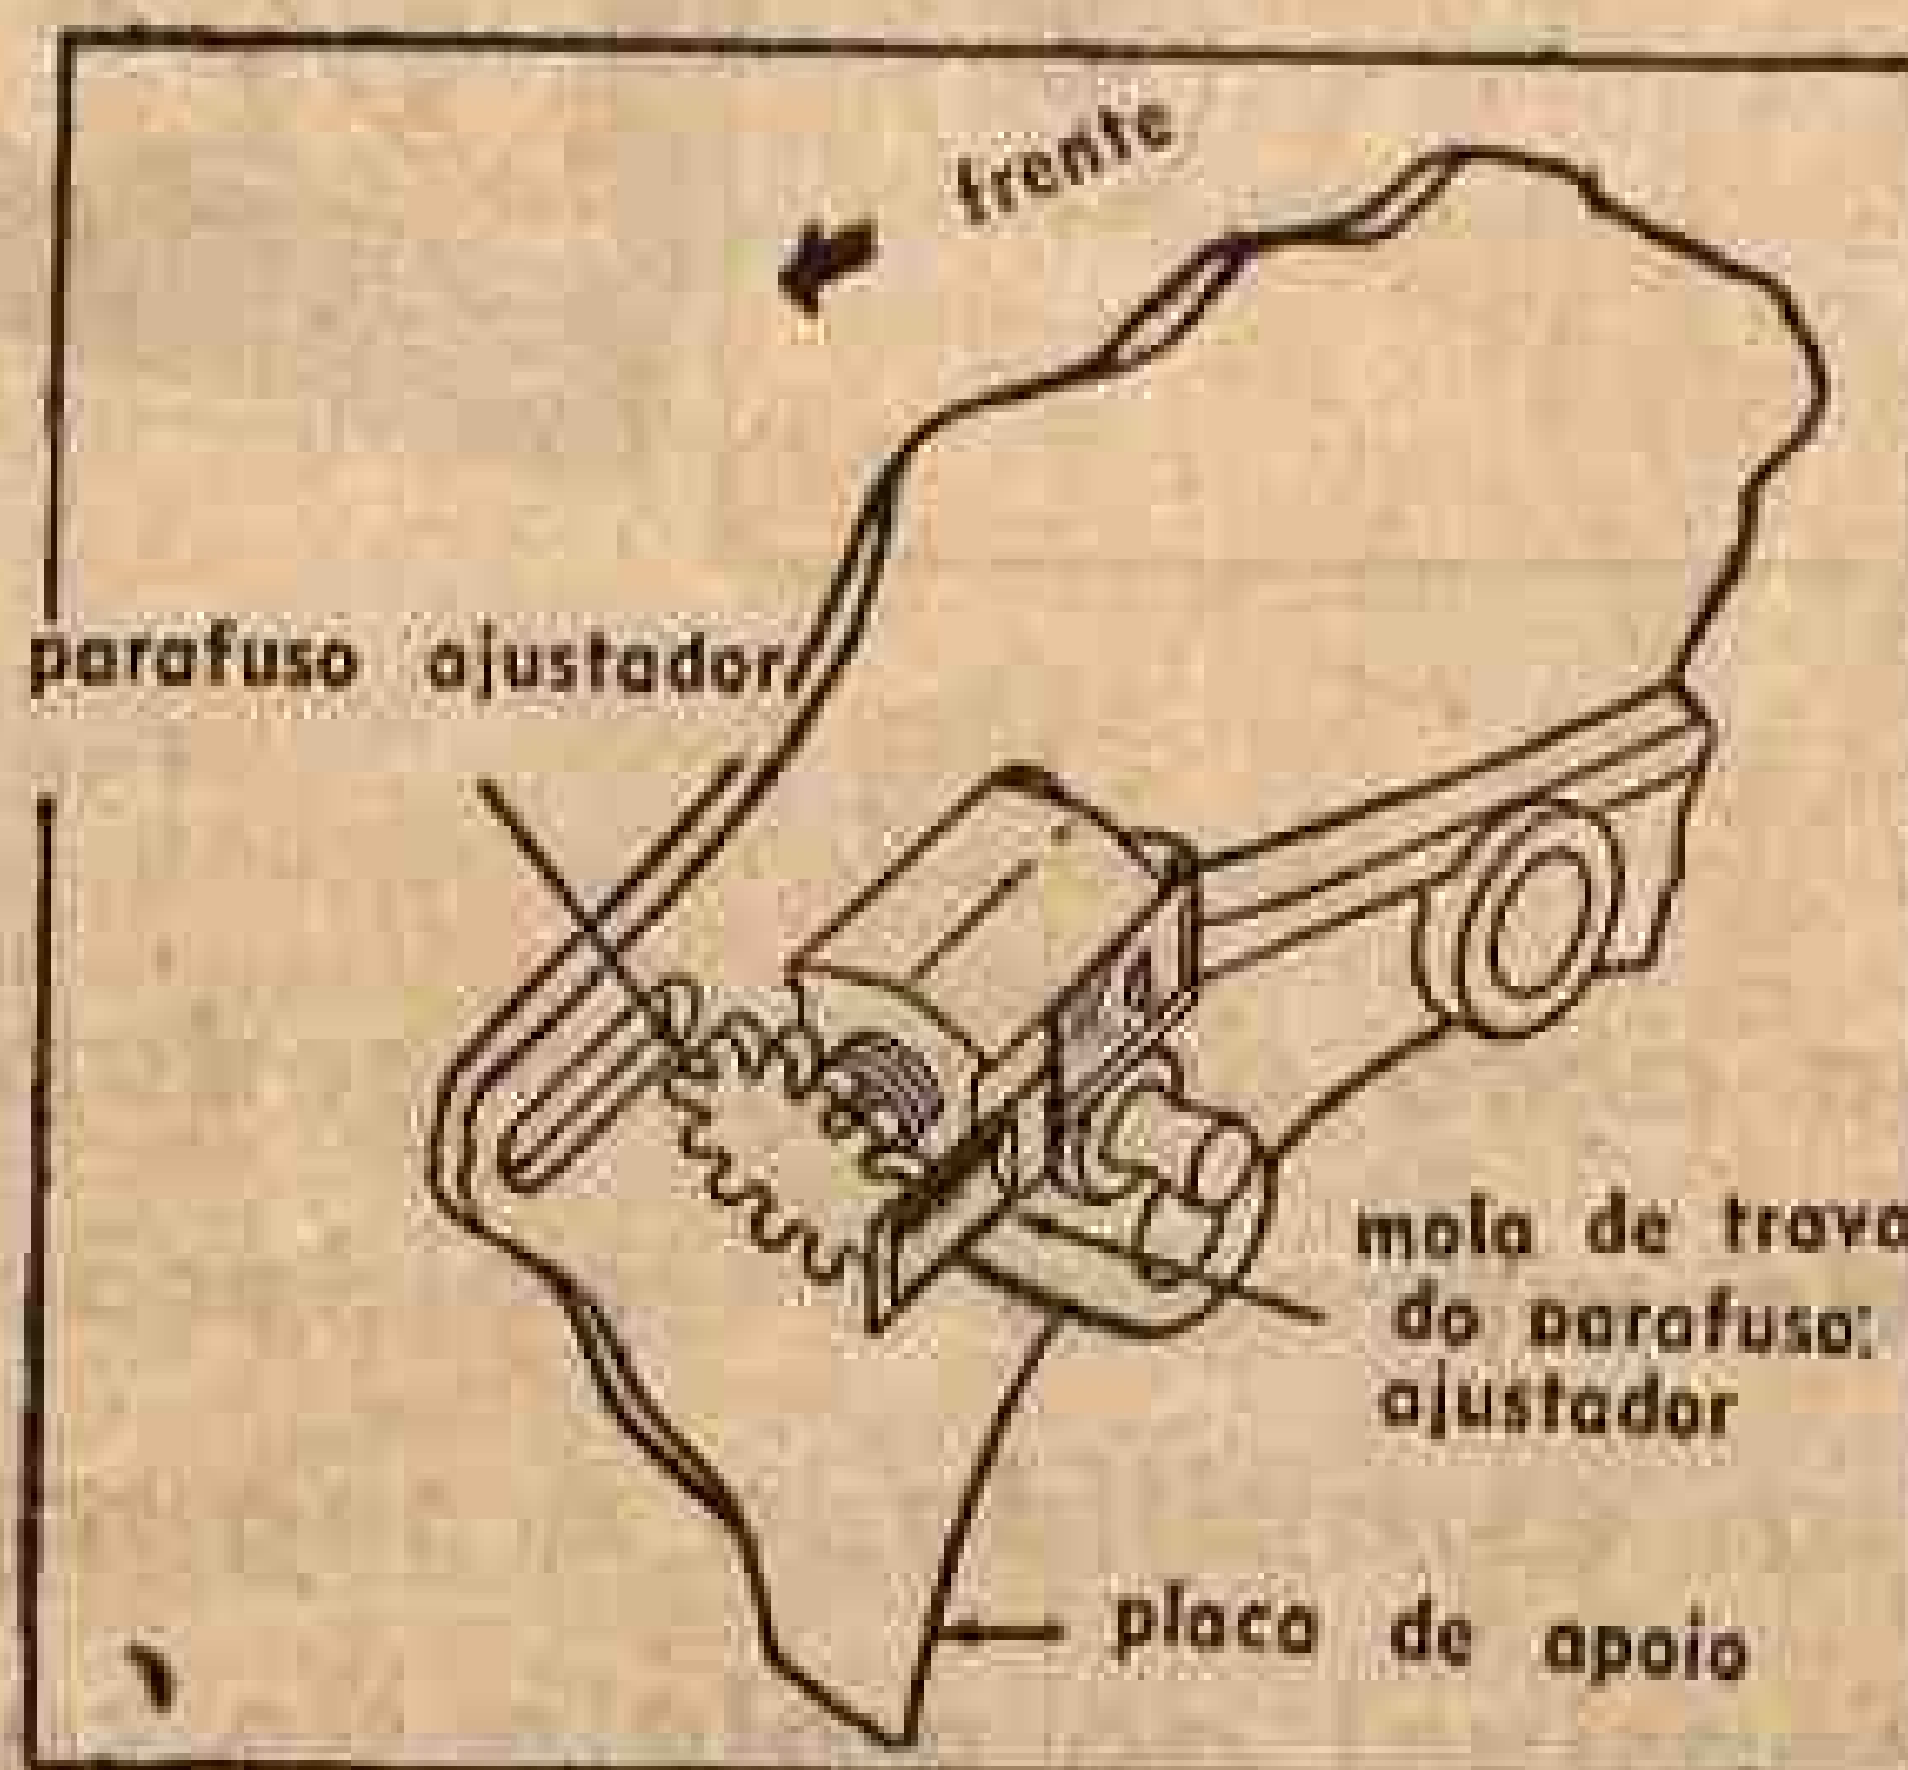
Montagem do parafuso ajustador e da mola de trava na placa de apoio.
